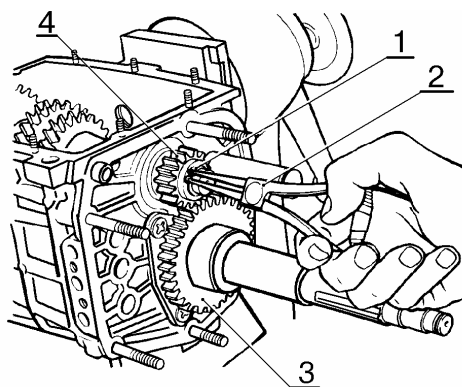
Снятие стопорного кольца шестерни заднего хода с промежуточного вала:
